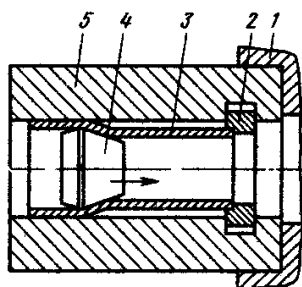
Обработка с размещением детали в жестком корпусе: 1 — опорная плита станка; 2 — раздвижная опора; 3 — деталь; 4 — инструмент; 5 — жесткий корпус
